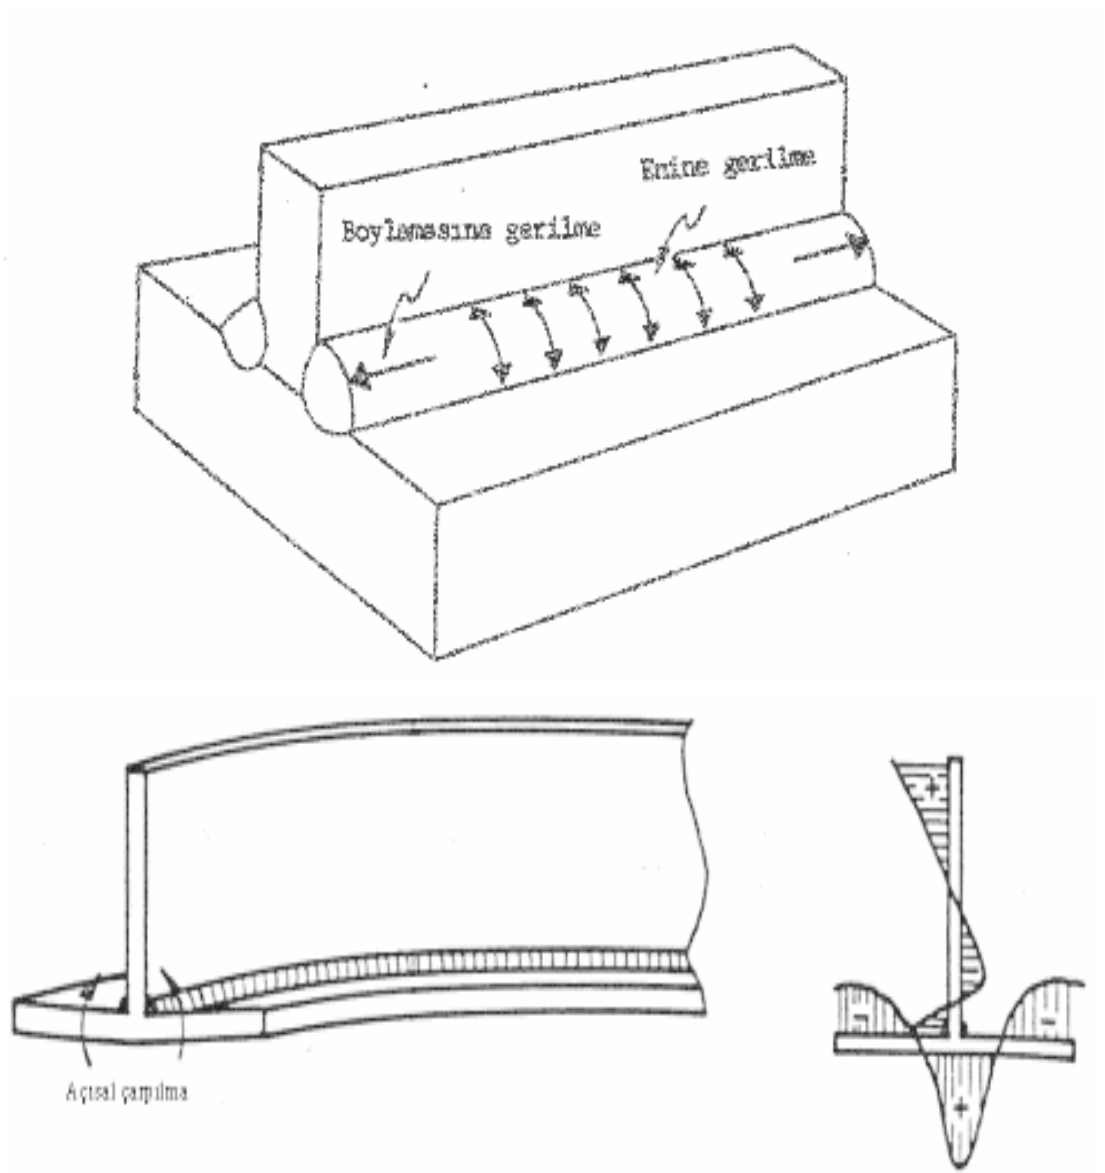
Bir kenar kaynağında kalıntı gerilmeler [28]
